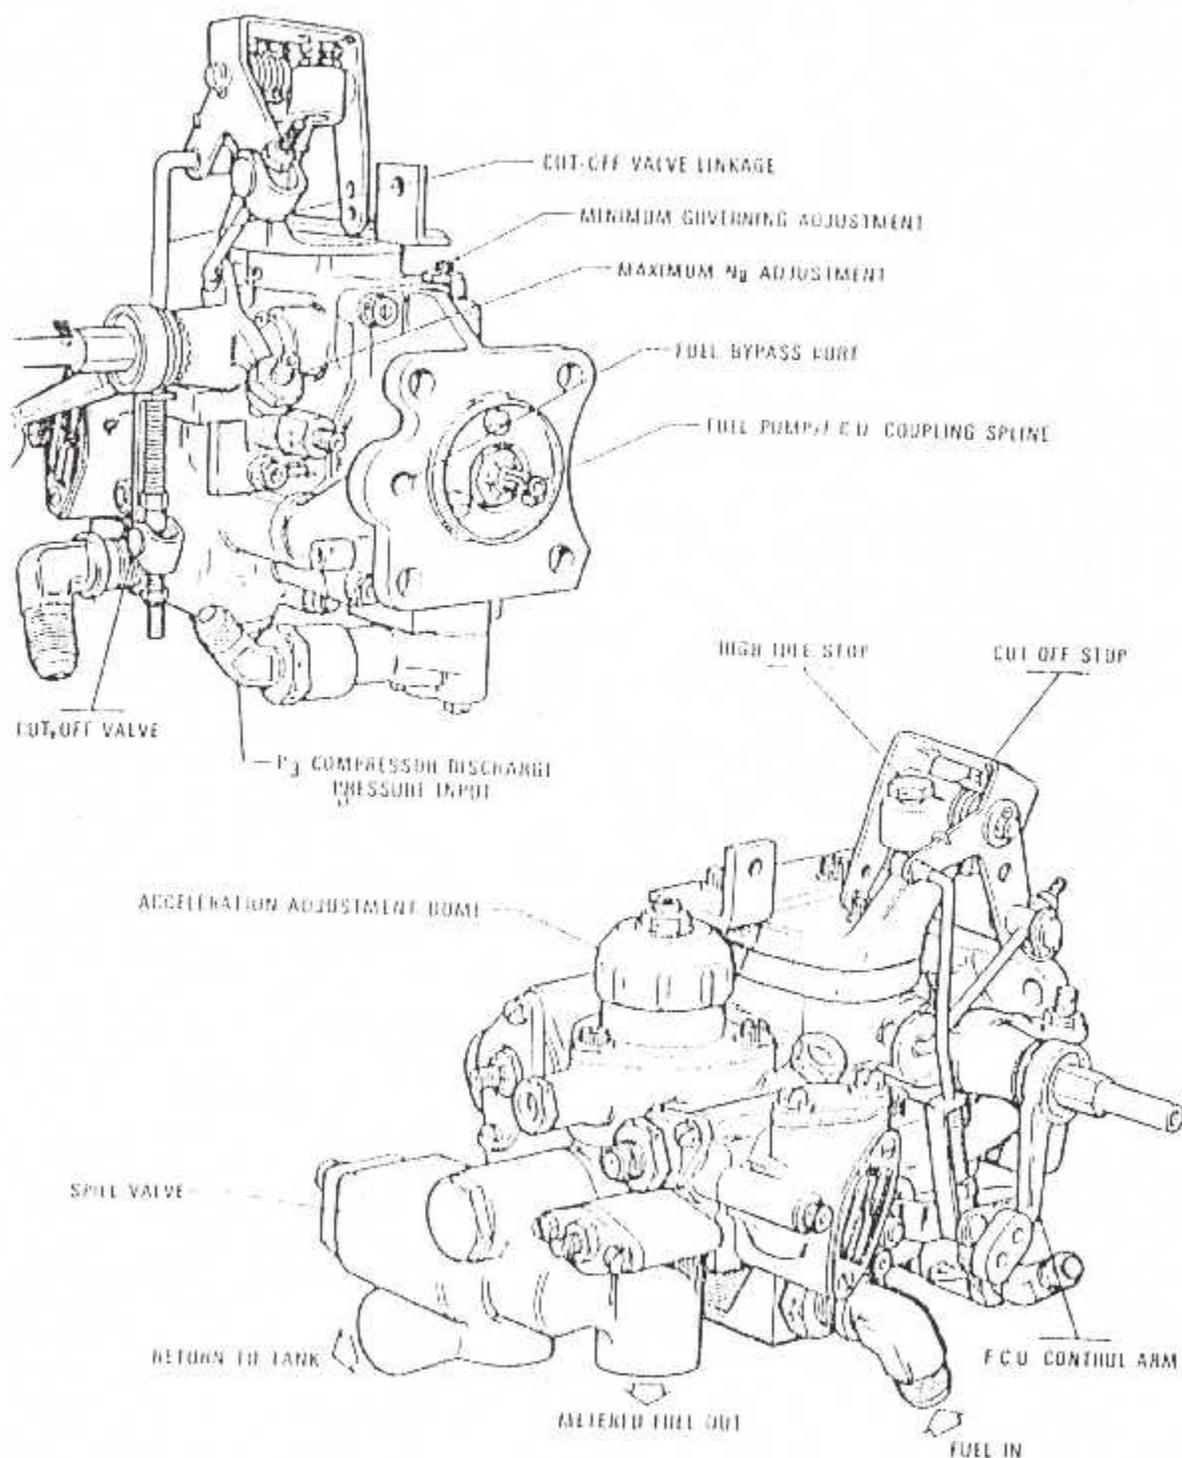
Régulateur principal de carburant du PT6A-41
